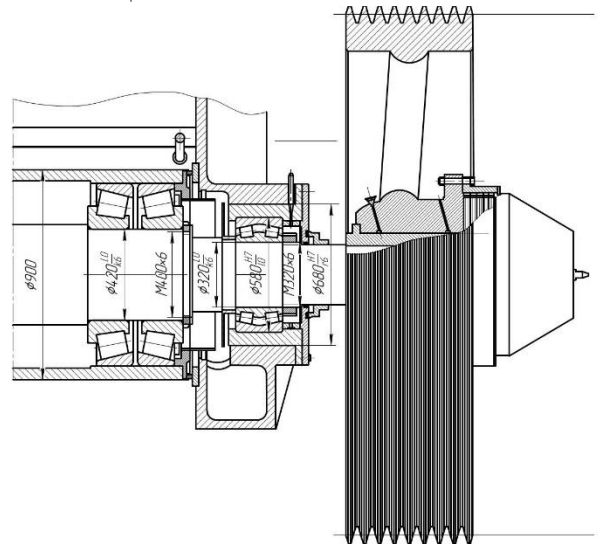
Переріз підшипникового вузла ексцентрикового вала шокової дробарки.
